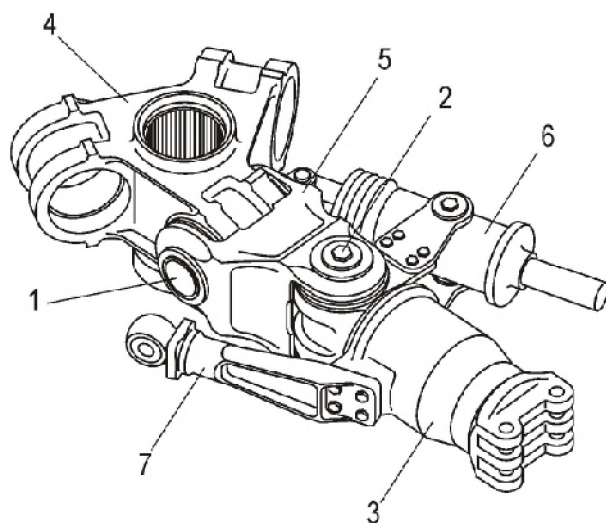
Шарнирная втулка НВ одновинтового вертолета Ми-2 с последовательностью расположения шарниров ГШ-ВШ-ОШ [25]: 1 – горизонтальный шарнир; 2 – вертикальный шарнир; 3 – осевой шарнир; 4 – корпус втулки; 5 – скоба; 6 – демпфер; 7 – рычаг поворота лопасти.
